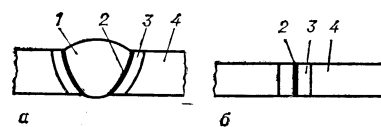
Сварное соединение: 1 — сварной шов; 2 — зона сплавления (а) или соединения при сварке давлением (б); 3 — зона термического влияния; 4 — прилегающий основной материал.
